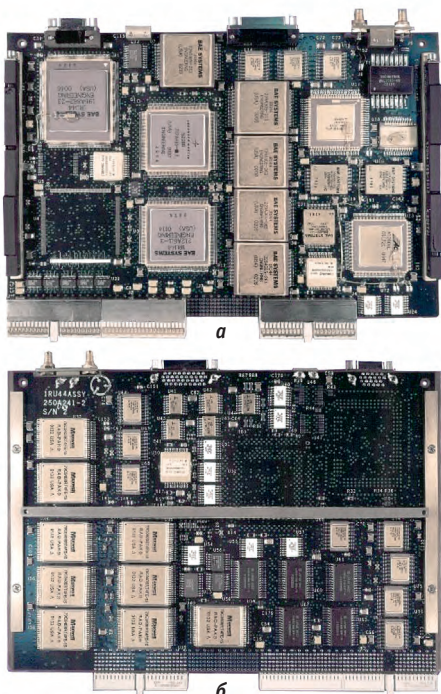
Одноплатный компьютер RAD6000 в формате CompactPCI 6U: а – вид сверху, б – вид снизу
